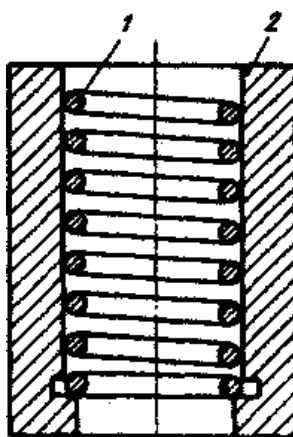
Приспособление для закалки пружин сжатия: 1 – пружина;
